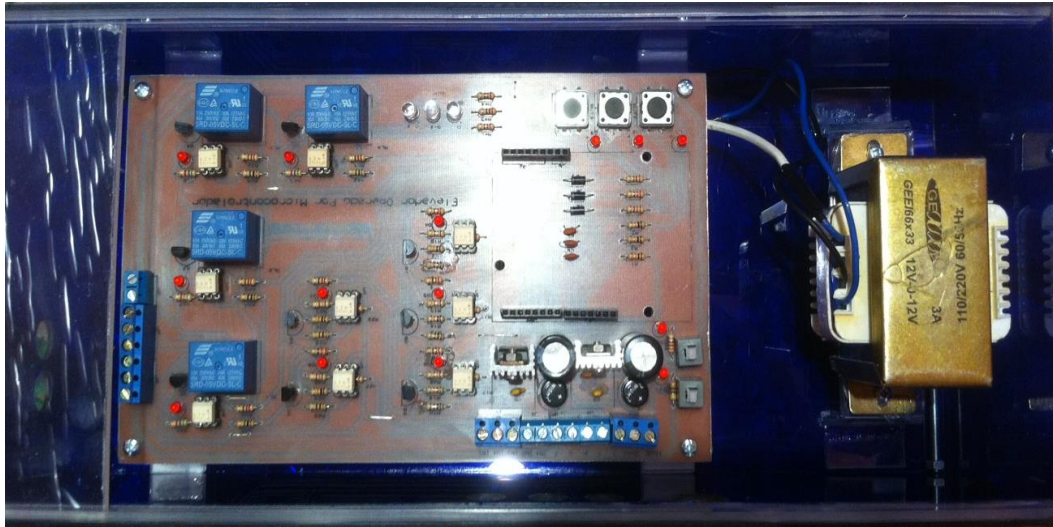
Placa PCB finalizada colocada en una caja de acrílico
